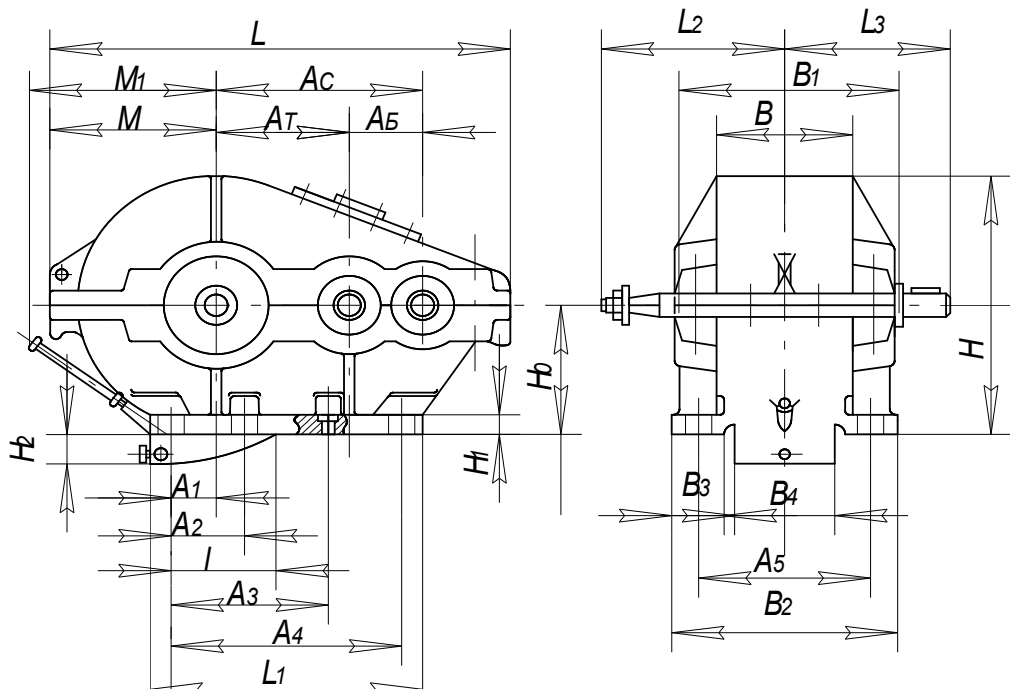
Схема размеров редукторов Ц2-650; Ц2-750
